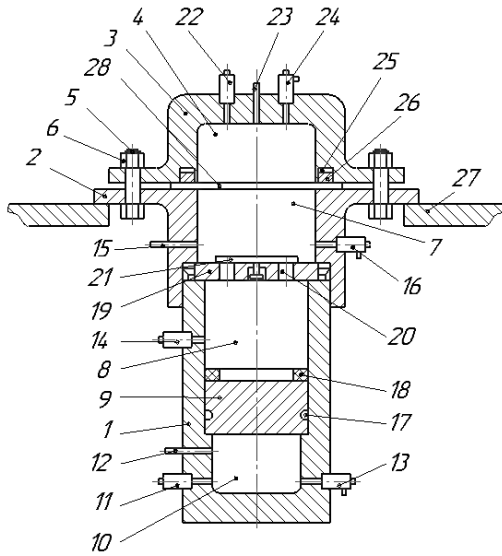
Устройство газовой штамповки: 1, 2 – части корпуса; 3, 4 – матрица и ее полость; 5 – болт; 6 – гайка; 7 – камера сгорания; 8 – рабочий цилиндр; 9 – поршень; 10 – дополнительная камера сгорания; 11, 14, 22 – впускные клапаны; 12, 15, 23 – свечи зажигания; 13, 16, 24 – выпускные клапаны; 17 – уплотнение; 18 – эластичная шайба; 19 – плита; 20 – отверстия; 21 – обратный клапан; 25 – кольцевая полость; 26 – кольцевой прижим; 27 – опора; 28 – заготовка
